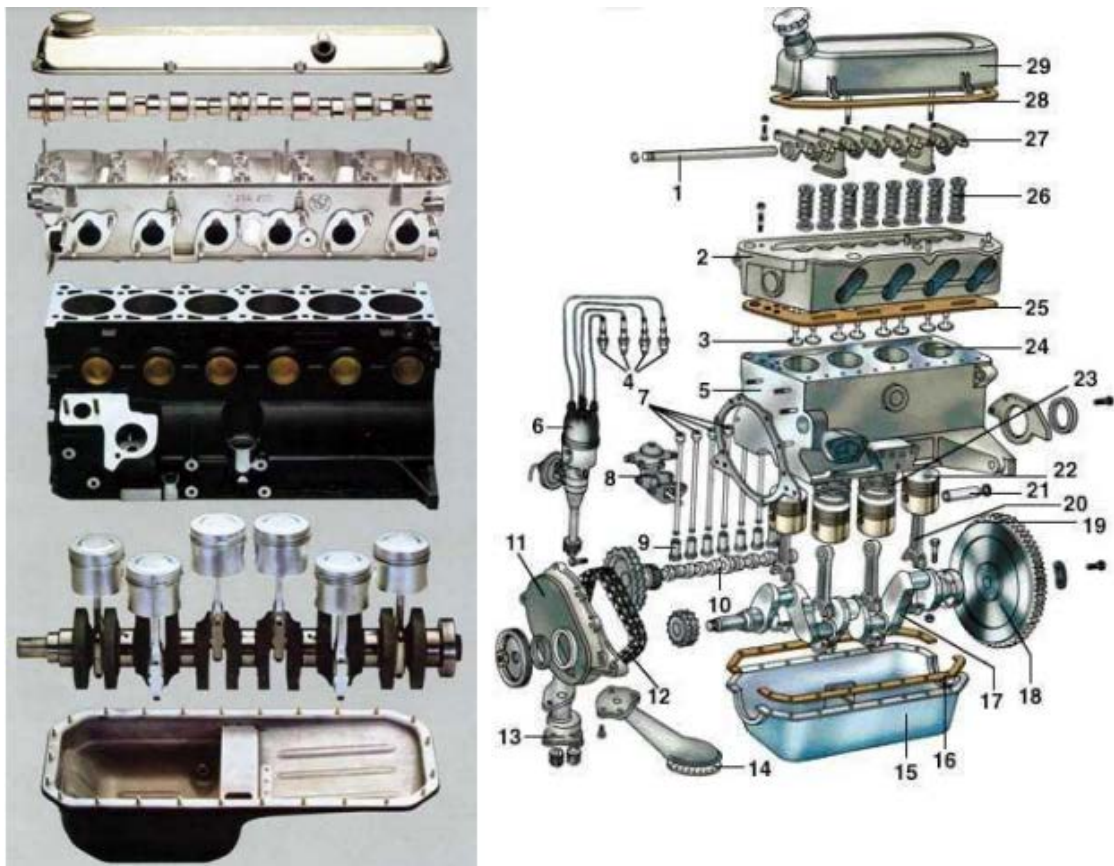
Vue éclatée d'un moteur à combustion interne
